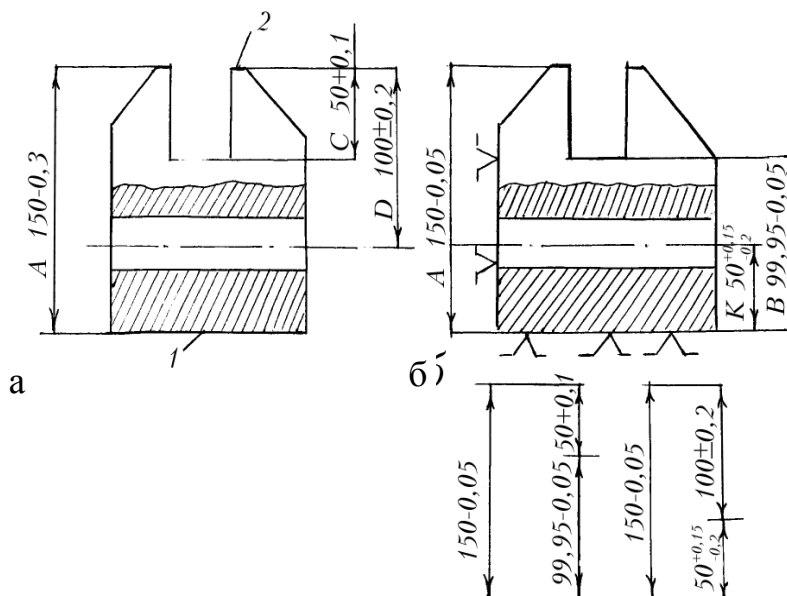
Креслення деталі (а) і ескіз обробки
